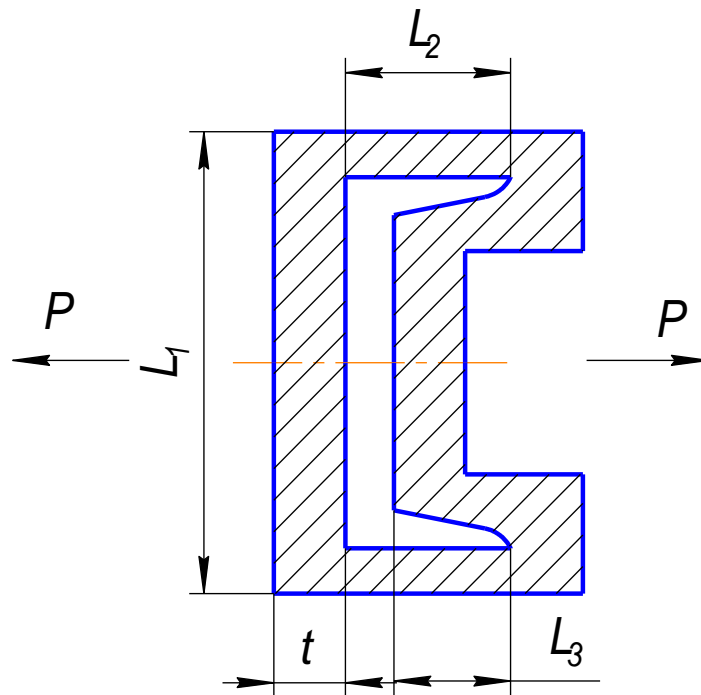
Розрахункова схема зварювального кріплення кронштейна до рами
